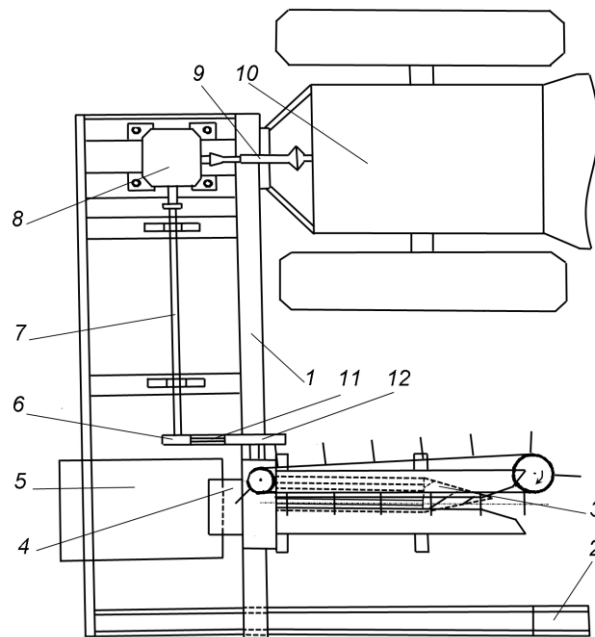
Схема экспериментальной установки (вид сверху): 1 - рама; 2 - лыжа; 3 –початкоотделяющий аппарат; 4 - лоток початков; 5 - емкость для сбора початков; 6 - приводной шкив-вариатор; 7 - вал; 8 - редуктор; 9 - карданный вал; 10 - трактор Т-40; 11 - клиноременная передача; 12 - ведомый шкив
